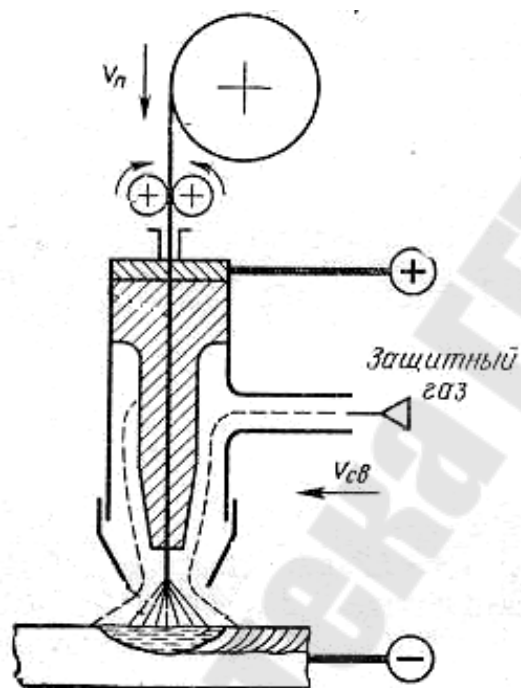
Схема аргонодуговой сварки.
